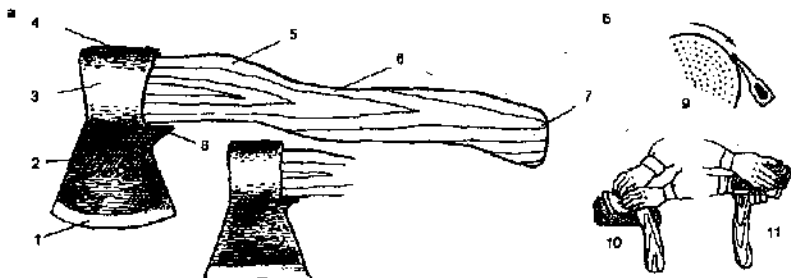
Название частей топора и топорика (а): 1 — лезвие; 2 — боек; 3 — проух; 4 — обух; 5 — топорик; 6 — бородка; 7 — захватная часть; 8 — хвост. Порядок точки топора (б); 9 — отточка на точиле; 10 — заточка на бруске; 11 — правка оселком
